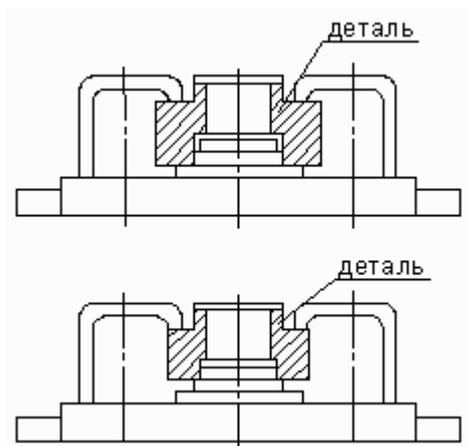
Схемы установки деталей на специальное приспособление для групповой обработки.
